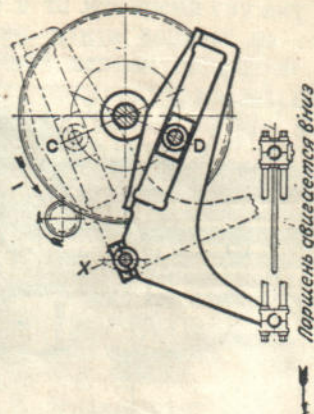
Передача от зубчатого колеса верхнему коленчатому рычагу и от рычага штанге.
